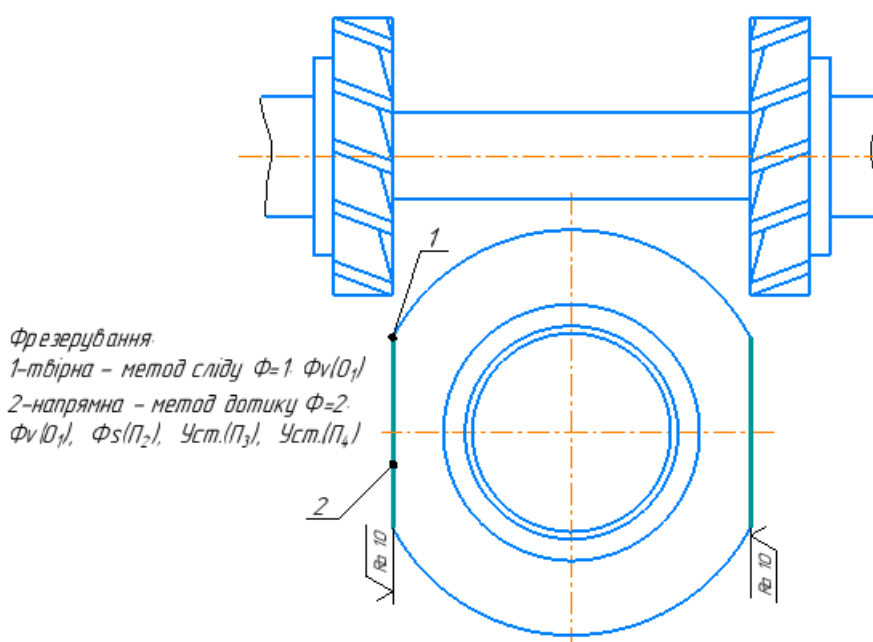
Формоутворюючі рухи при обробці набором фрез
